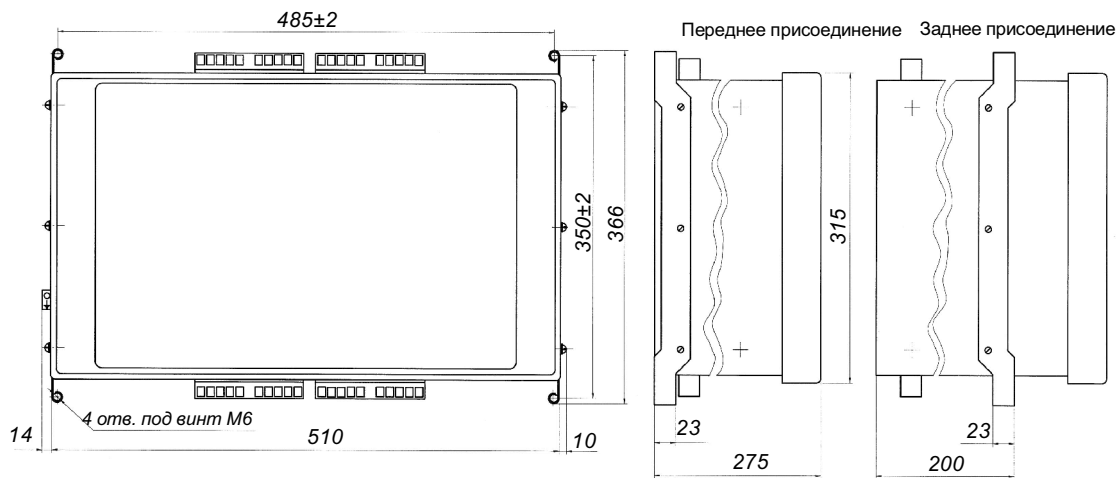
Габаритные, установочные размеры блока типа БЭ 1104.
